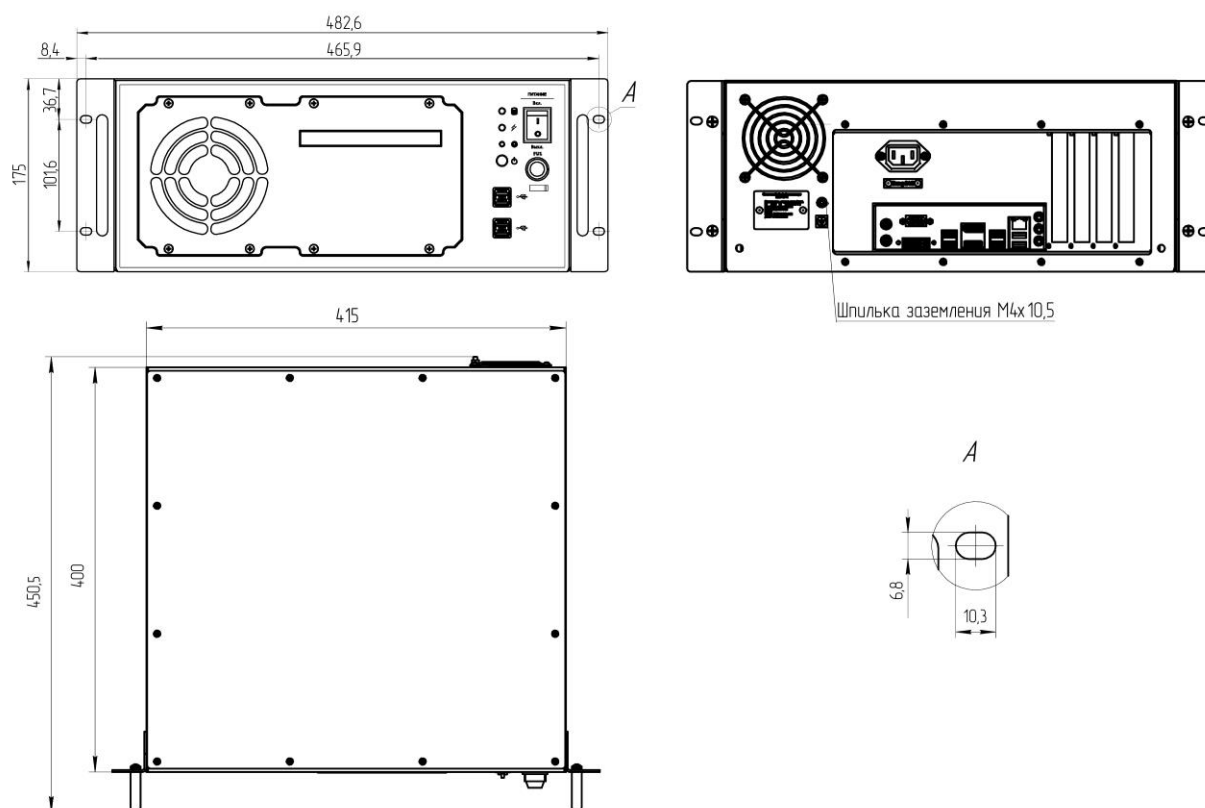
Габаритные размеры изделия типа СБК-19-4
